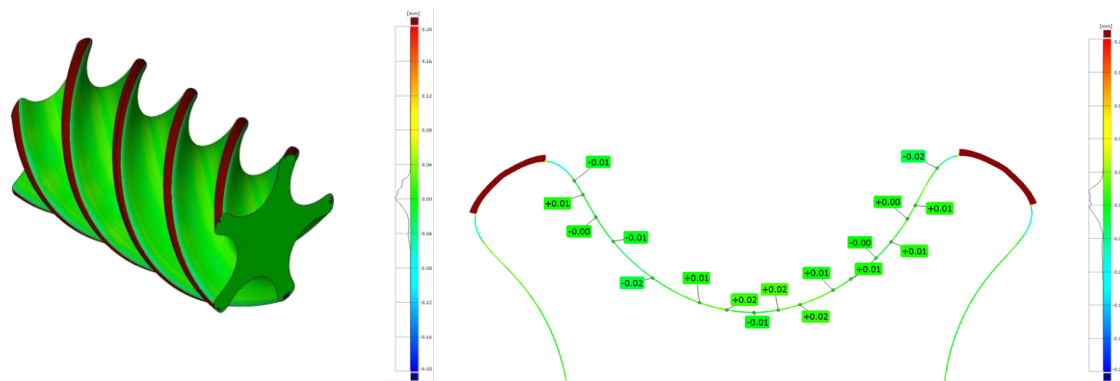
Desviación dimensional del compresor de tornillo sin fin hembra simétrico.
